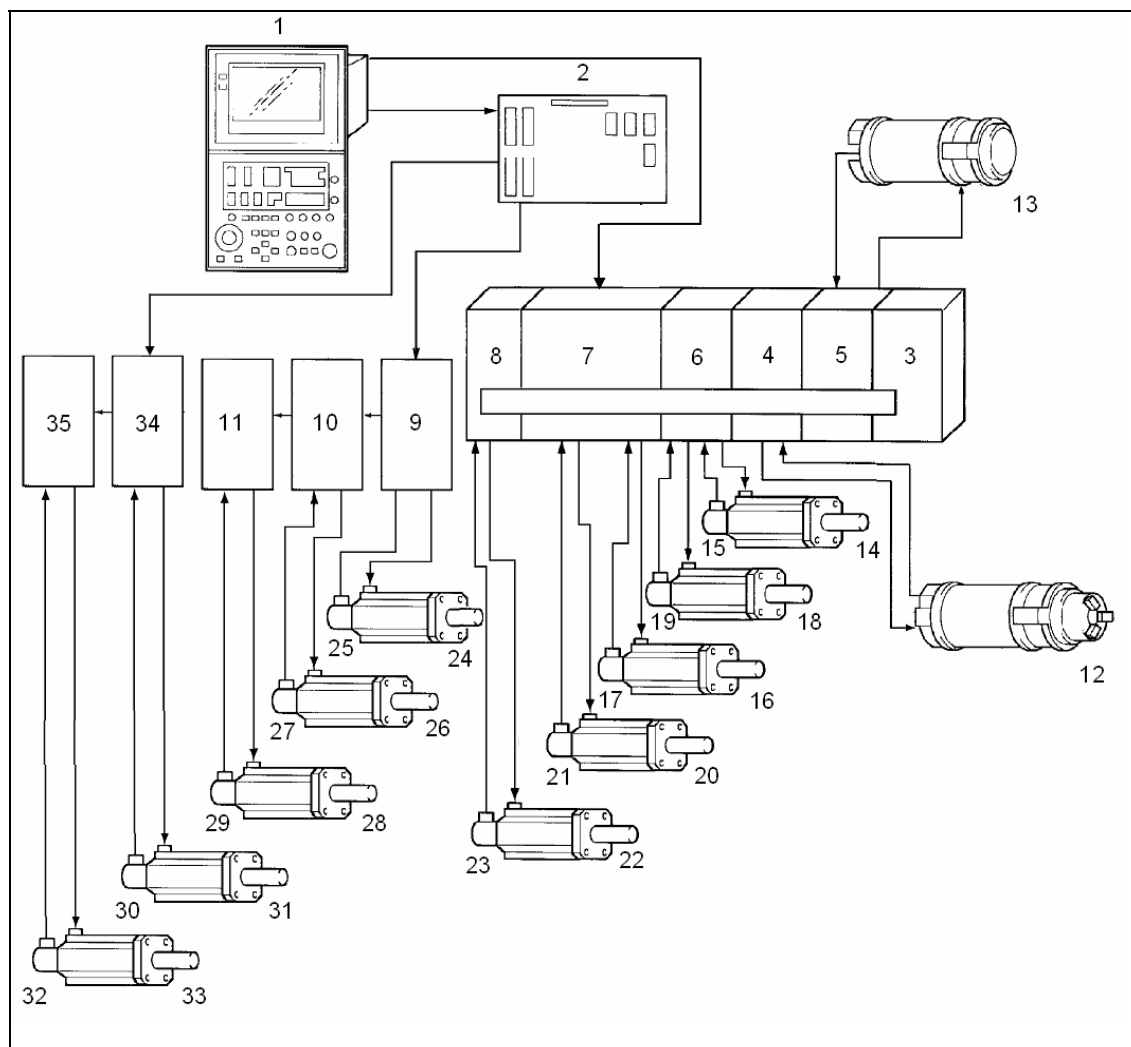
УЧПУ (для станка INTEGREX i-150)
